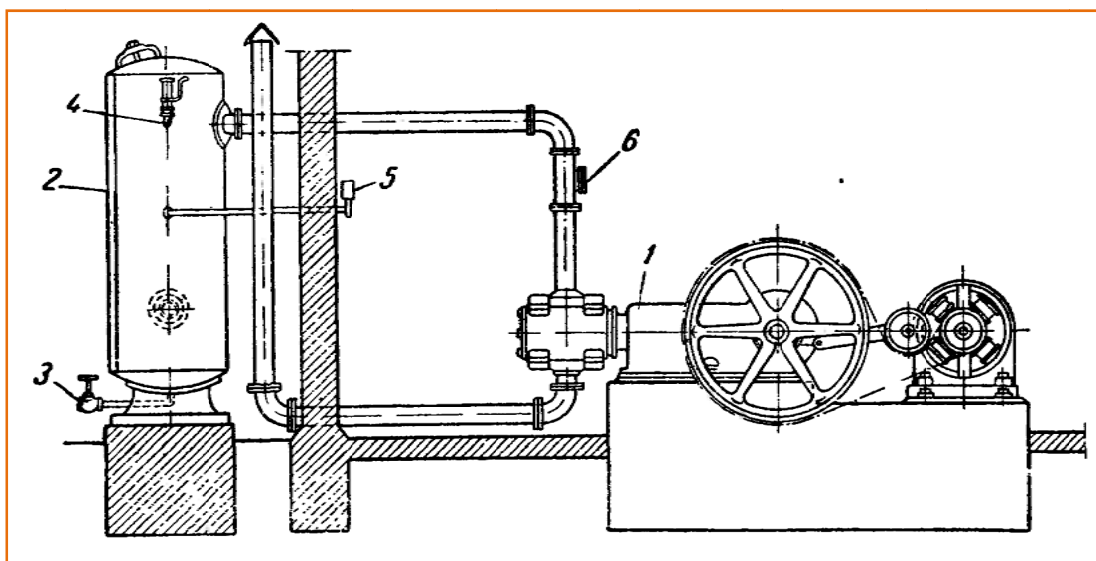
Схема установки поршневого компресору: 1 – компресор, 2 – повітрозбірник (ресивер), 3 - спускний кран, 4 - запобіжний клапан, 5 – манометр, 6 – зворотний клапан
